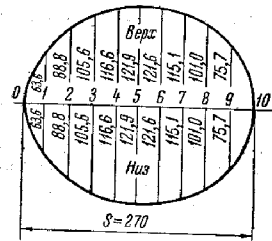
Развертка отверстия в стволе сварного тройника.
